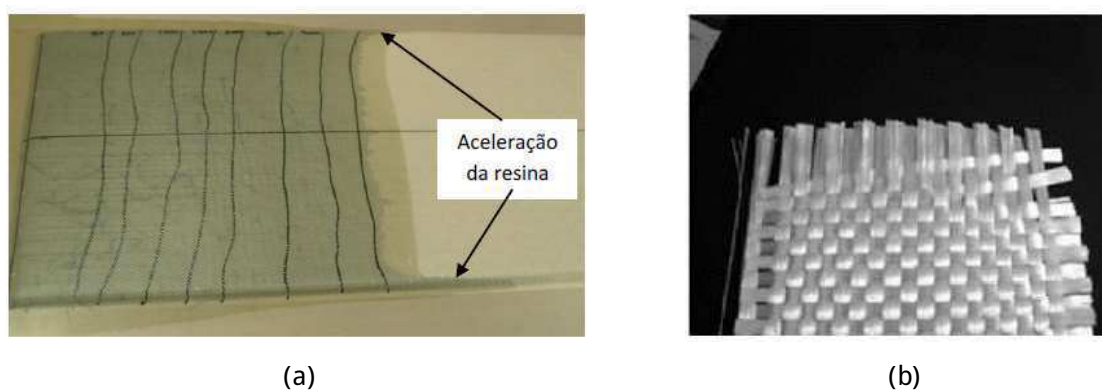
Processo de Moldagem por Transferência de Resina.
